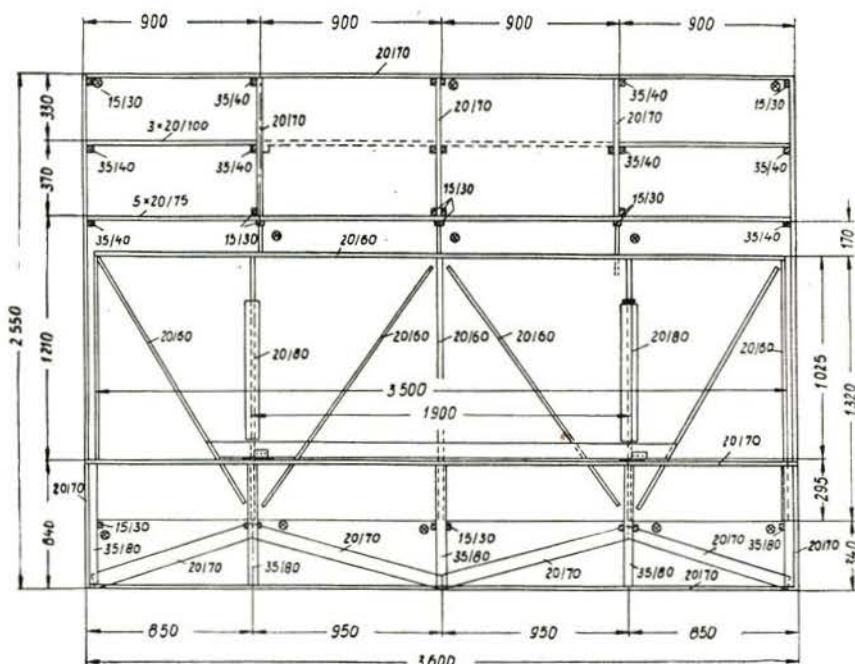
Draufsicht auf Konstruktion des Klappschranks einschließlich eingehängter Grundplatte
